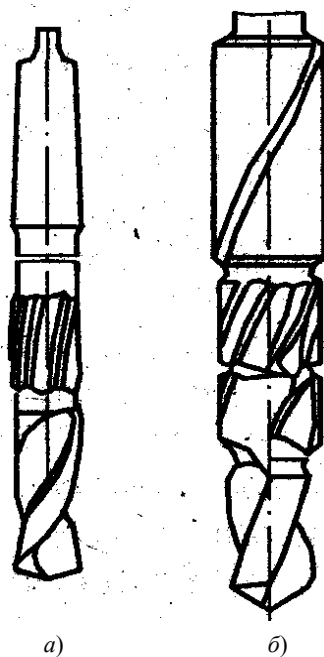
Сверло-развёртка (а) и сверло-зенкер-развёртка (б)
